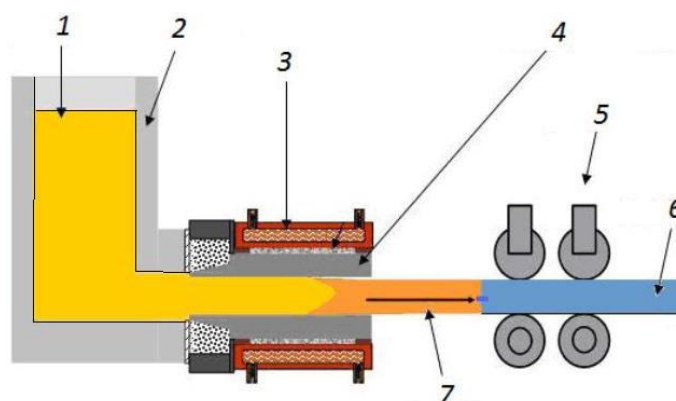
Схема ГМПЛЗ [1, 2]: 1 – расплав; 2 – тигель; 3 – медное охлаждающее устройство; 4 – графитовый кристаллизатор; 5 – вытяжное устройство; 6 – затравка; 7 – непрерывнолитая заготовка
